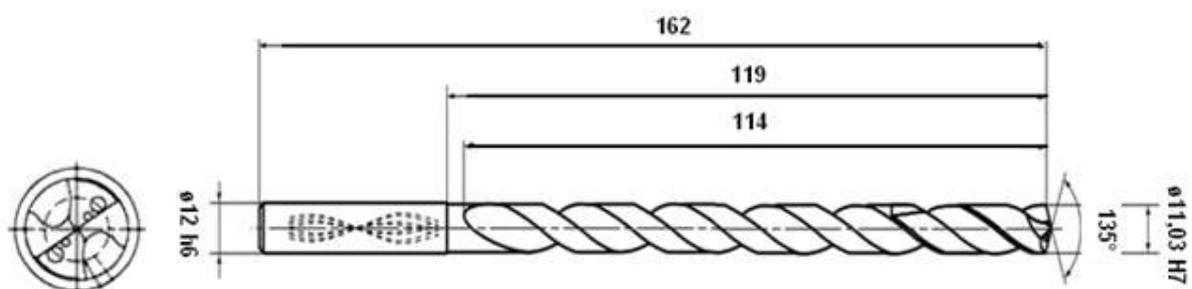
Hartmetallbohrer mit 4 Kühlbohrungen
